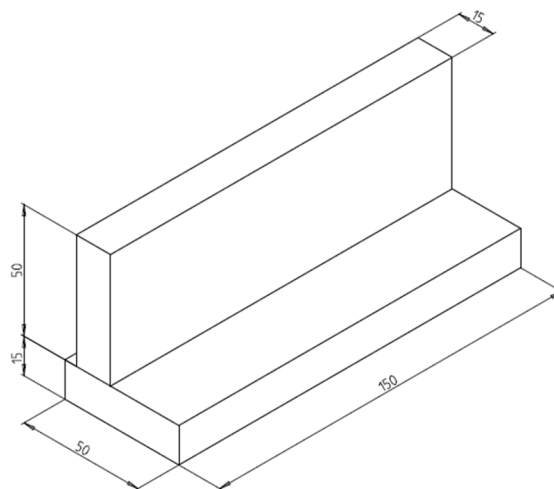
Maßzeichnung für die Kehlnahtschweißungen
